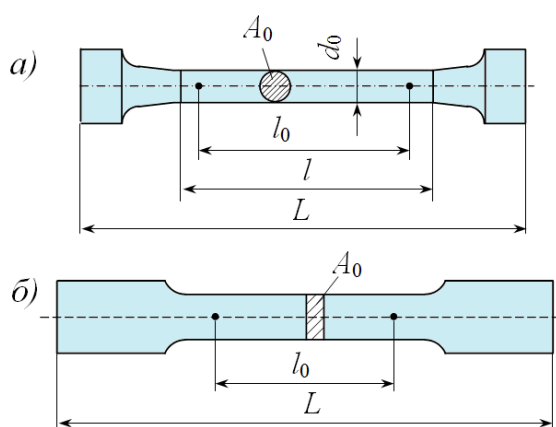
Образцы для испытания на растяжение: а) – цилиндрический образец; б) – плоский образец
